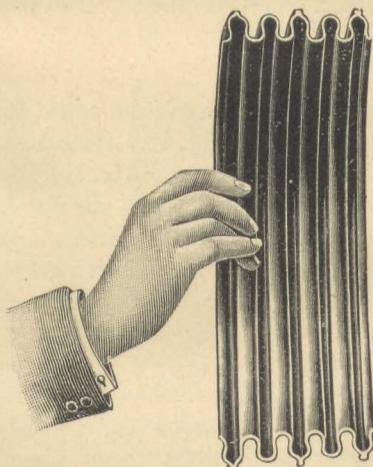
Innenansicht eines geschweißten Metallschlauches von der lichten Weite von 200 mm.
